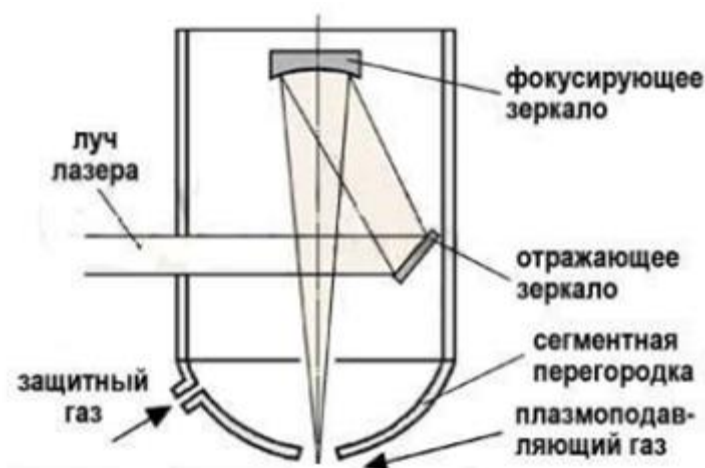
Схема лазерно-дуговой технологии сварки
